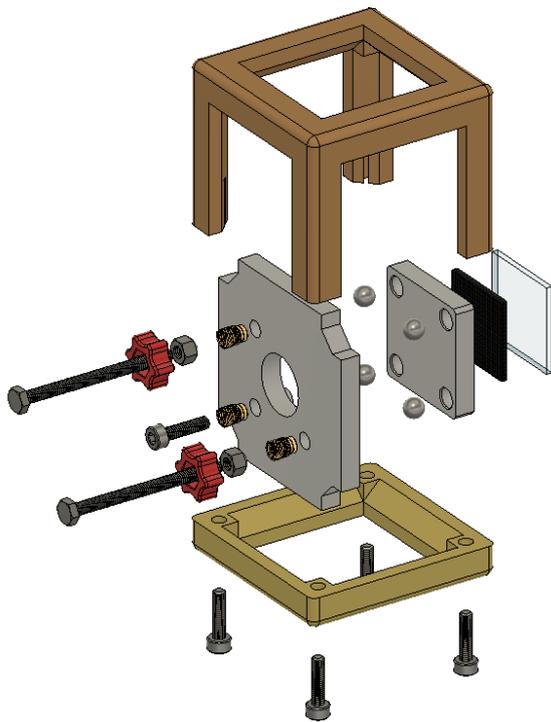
Explosionsansicht des 90°-Spiegelwürfels
